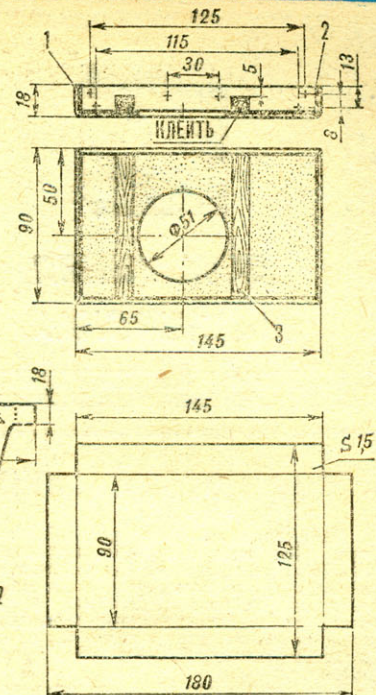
Опорная рамка в сборе: 1 — корпус рамки, 2 — кожа, 3 — бруски опорные.
